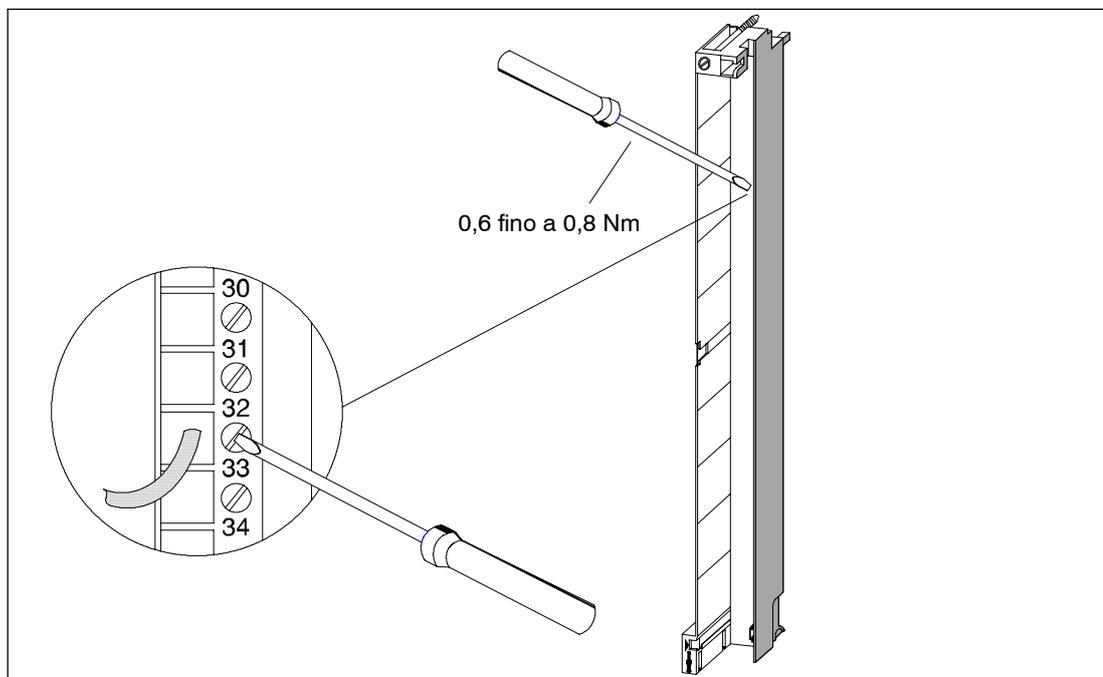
Cablaggio del connettore frontale con tecnica a vite
